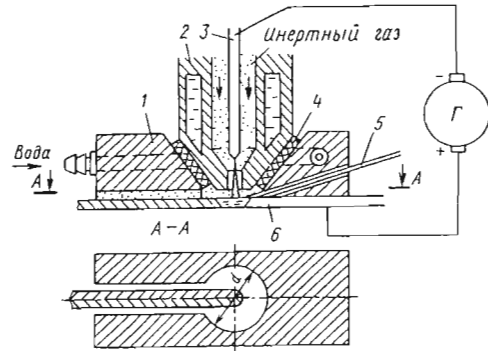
Схема головки для сварки закрытой сжатой дугой:
